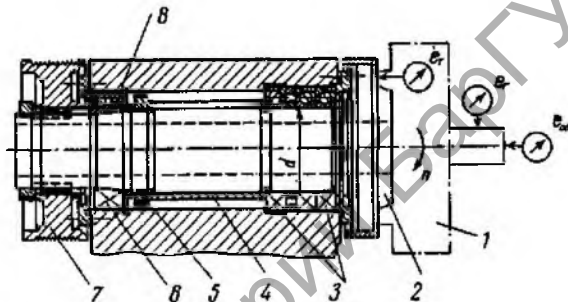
Типовая конструкция шпиндельного узла токарного станка
